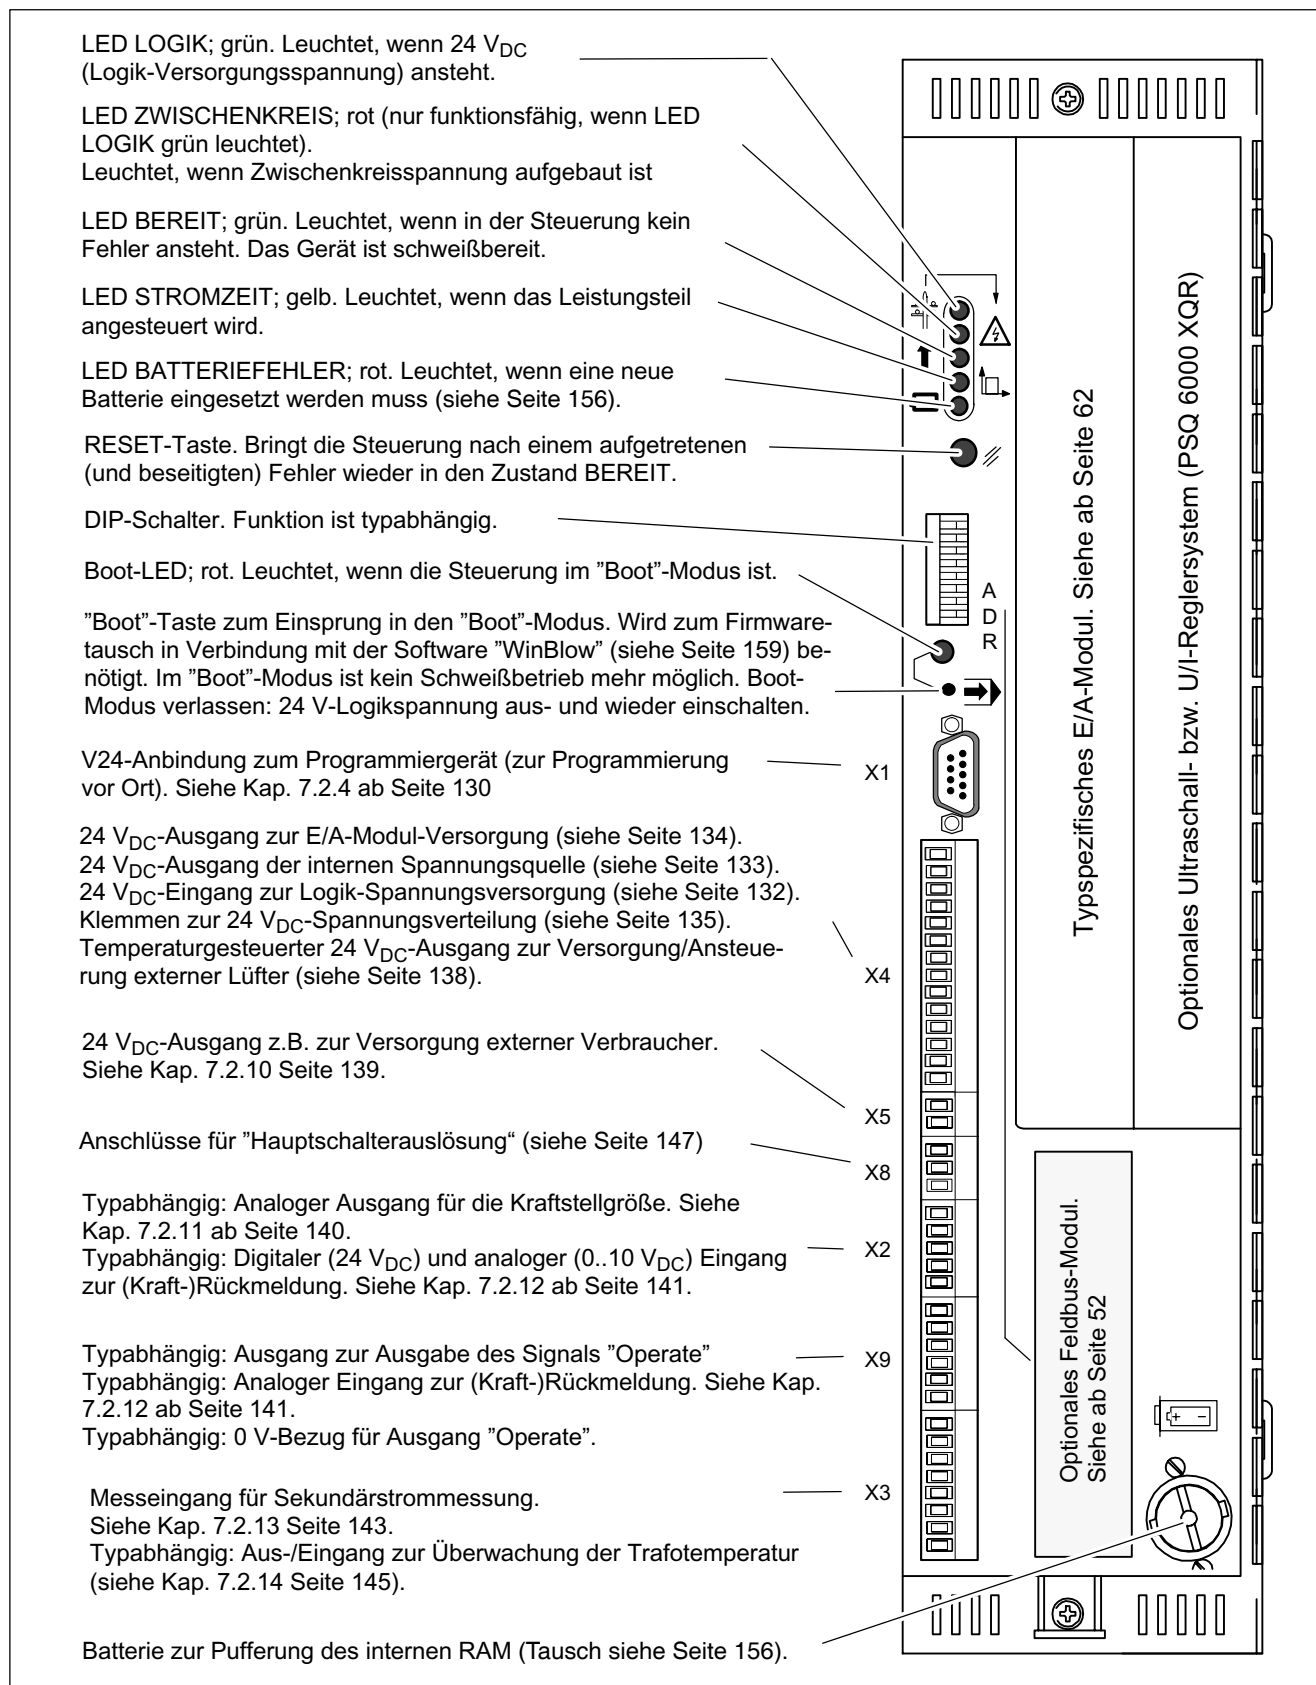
Teil-Frontansicht PSI 6x00.xxx
